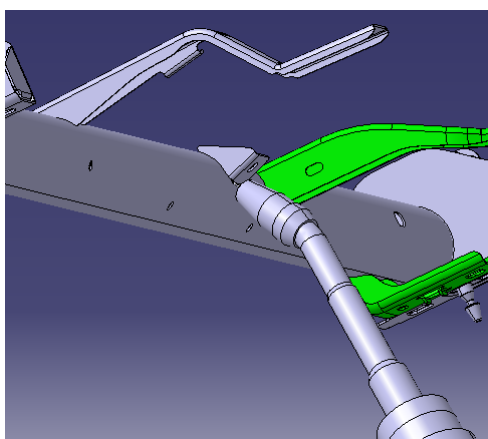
Antorcha de soldadura posicionada para dar un cordón entre dos componentes del producto. Fuente: Interob (2016).
